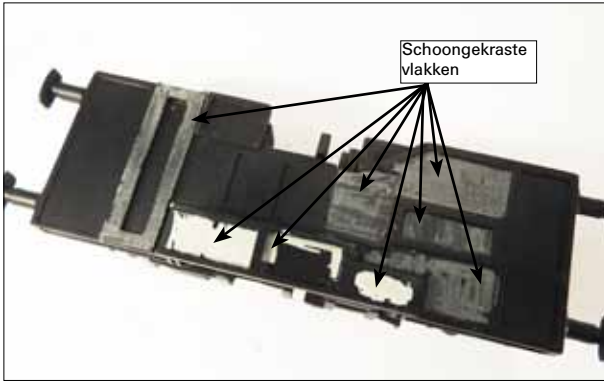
Schoongekraste vlakken t.b.v. betere hechting
